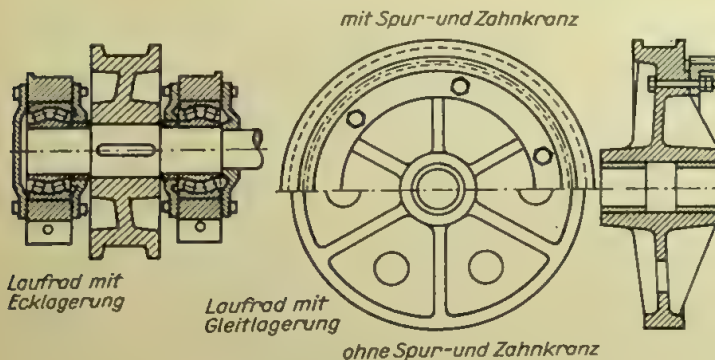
Laufradausführungen mit Eck- und Gleitlager
